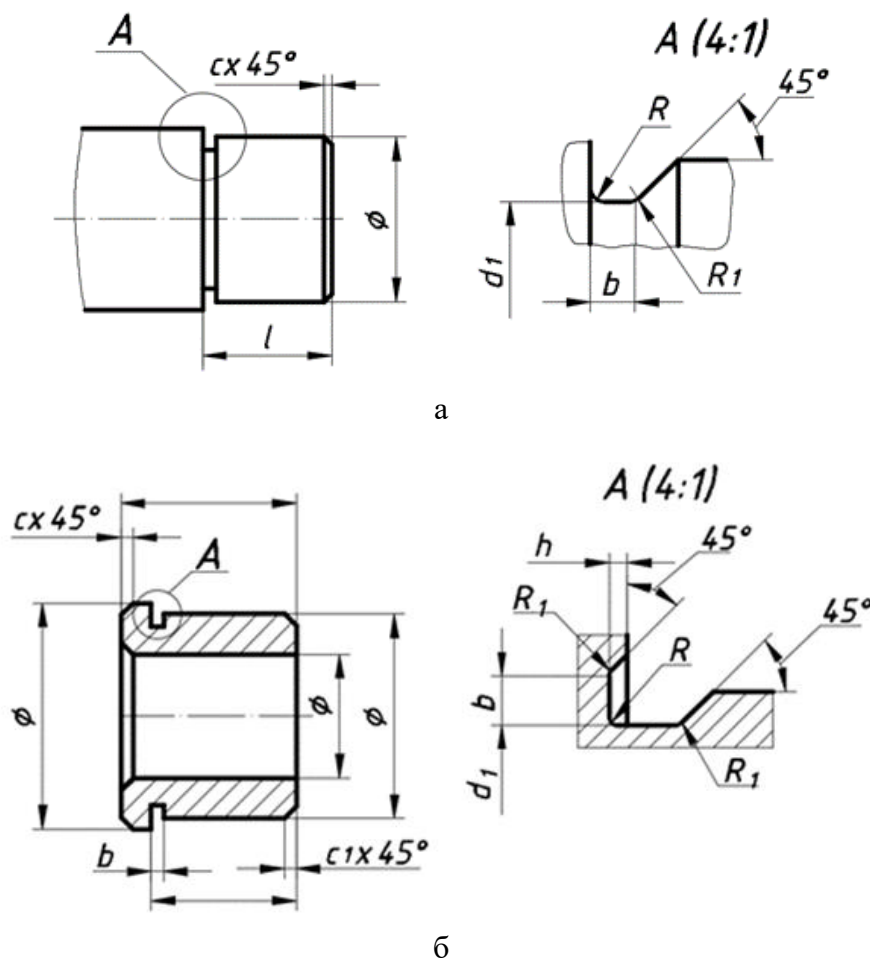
Образец выполнения канавки для выхода шлифовального круга: а-шлифование по наружному цилиндру; б- шлифование по наружному цилиндру и торцу.
